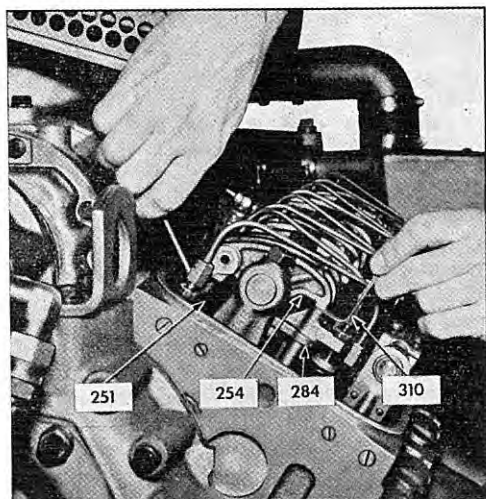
Réglage du jeu des soupapes (4 soupapes) sans ressort sous le balancier
